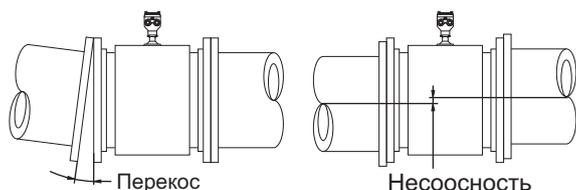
Перекос и несоосность трубопроводов, подсоединяемых к расходомеру
